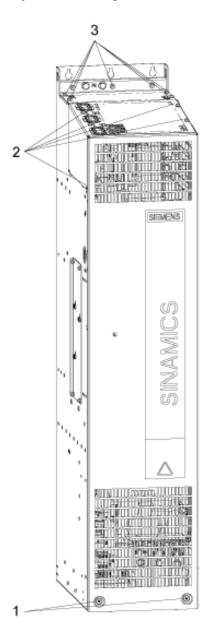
Montaje del Braking Module en un Power Module de tamaño GX: pasos 1 - 3
